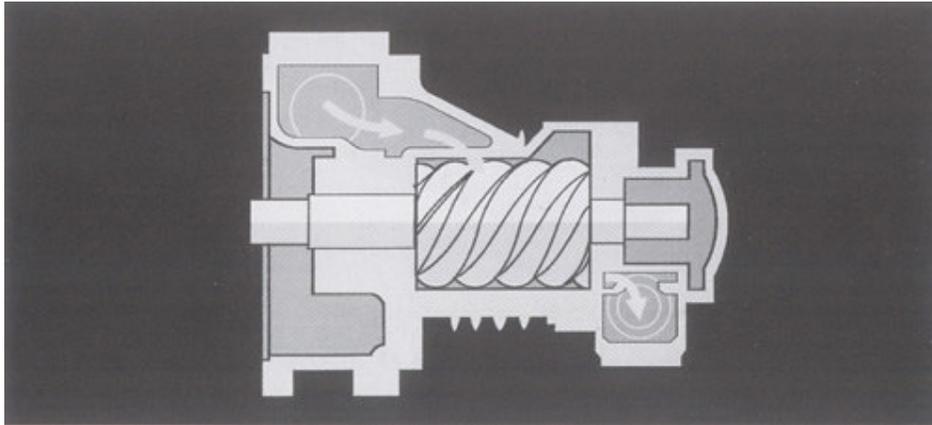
Esquema de compresor de simple tornillo rotativo.
